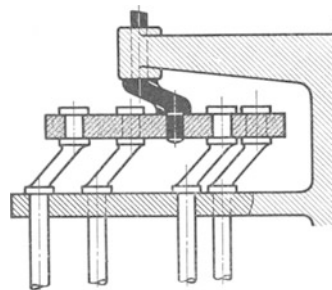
Eine große Zahl Blindwellen als Bohrspindeln einer Mehrspindelbohrmaschine.
